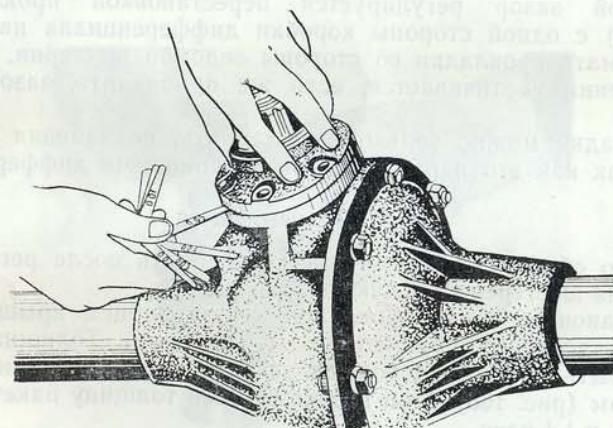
Замер зазора между крышкой подшипника и картером для подбора прокладок
